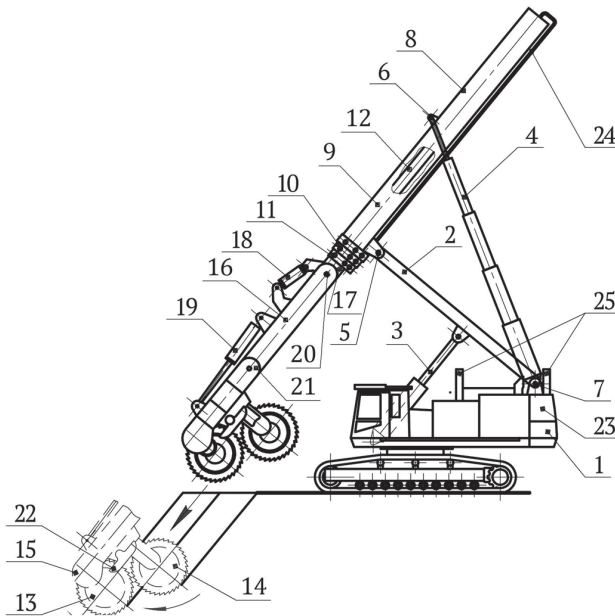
Фрезерная установка при нарезании щелей на откосе уступа: 1 – одноковшовый экскаватор; 2 – стойка; 3 – гидроцилиндр подъема стойки; 4 – телескопический гидроцилиндр; 5, 6, 7 – шарниры; 8 – телескопическая двухблочная стрела; 9 – корневая секция стрелы; 10 – промежуточная секция; 11 – головная секция; 12 – выдвижные гидроцилиндры; 13 – верхняя дисковая фреза; 14 – нижняя дисковая фреза; 15 – оголовок верхней фрезы; 16 – средняя часть оголовка; 17 – выдвижной участок оголовка; 18 – гидромеханизм преломления среднего участка оголовка; 19 – гидромеханизм преломления оголовка; 20, 21 – шарниры; 22 – опорные лыжи; 23 – насосная станция; 24 – телескопические трубопроводы; 25 – опорные кронштейны
